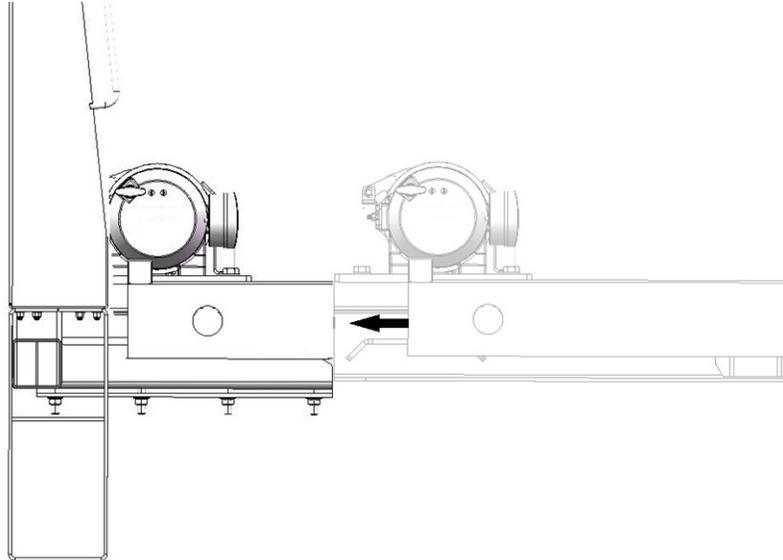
PLANCHER DE LA PLATEFORME EN POSITION VERROUILLÉE
